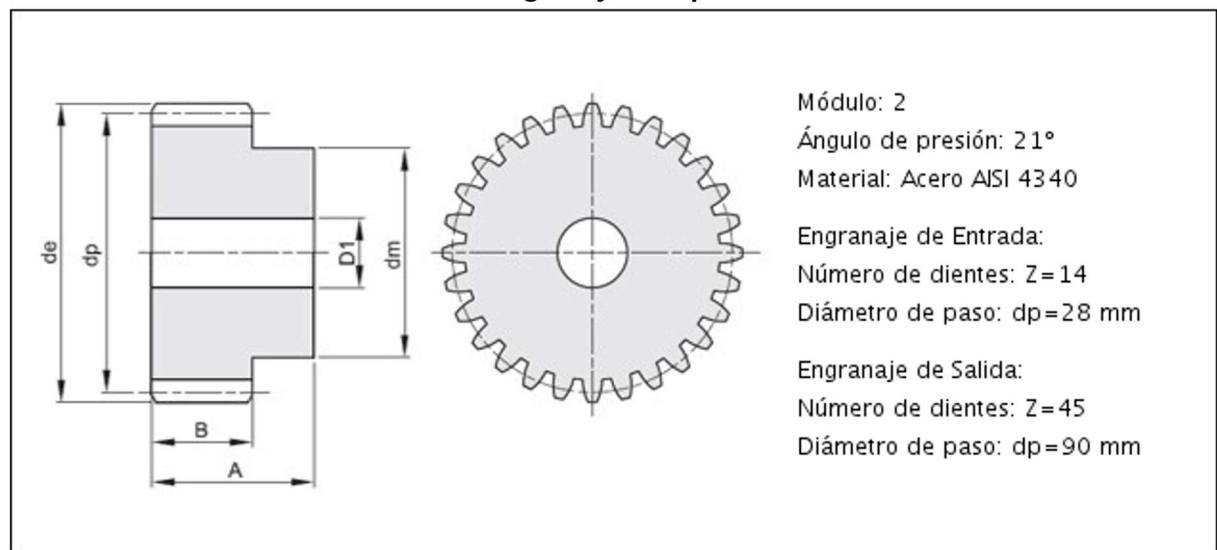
Engranajes de la etapa 2 de la caja reductora 2
